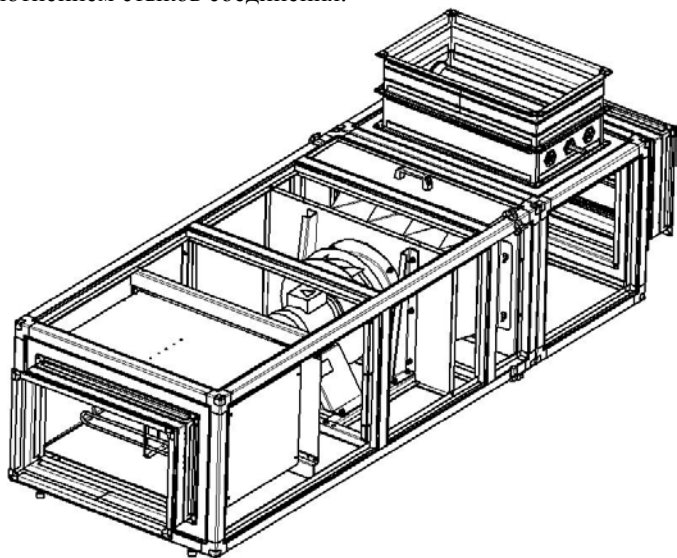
Схема монтажа секции смешения (пример для установки напольного с верхом)
